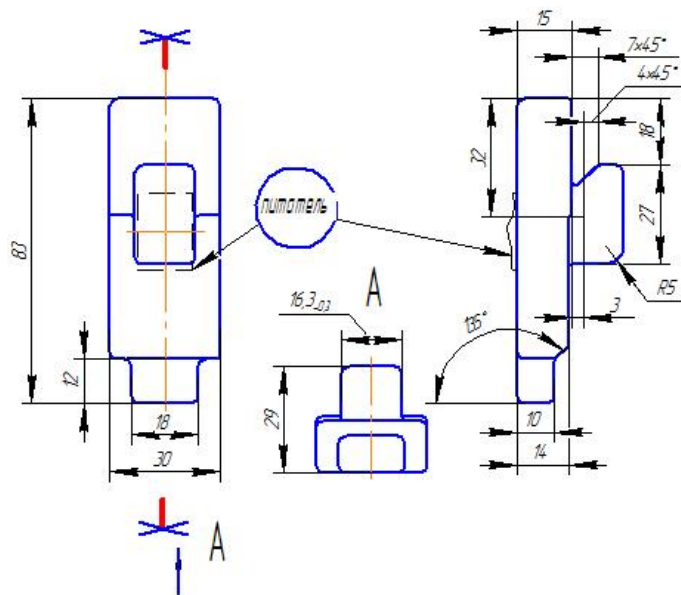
Эскиз отливки с поверхностью разъема пресс-формы.
